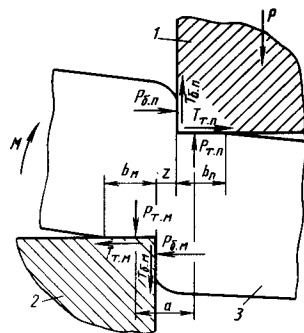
Схема сил, действующих на пуансон и матрицу со стороны деформируемой заготовки на стадии пластического сдвига при вырубке—пробивке: 1 — пуансон; 2 — матрица; 3 — отделяемая часть заготовки
